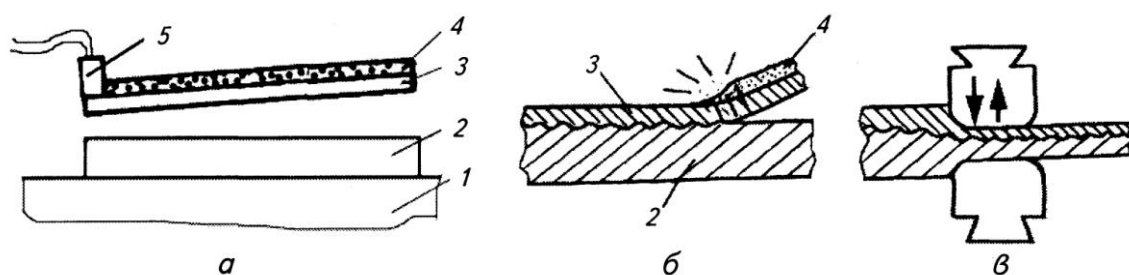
Схема плакирования металла методом сварки взрывом:
